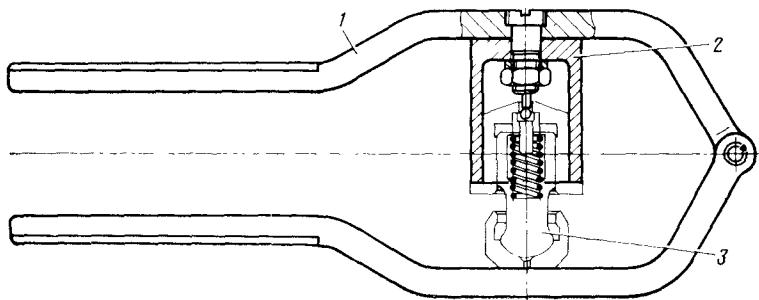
Приспособление для удаления масла из гидротолкателя:
